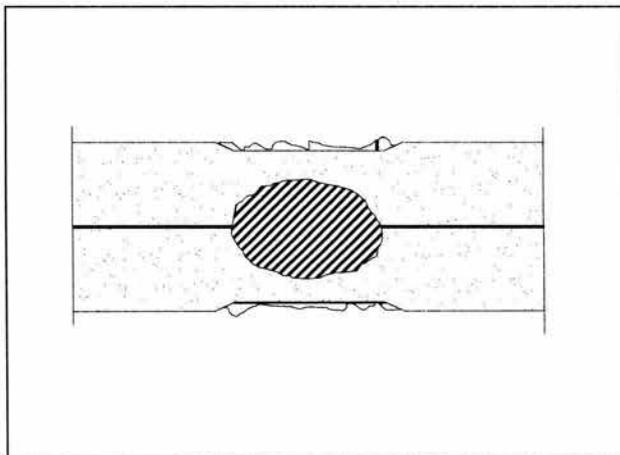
Soldadura incorrecta con residuos de material quemado en la superficie.
